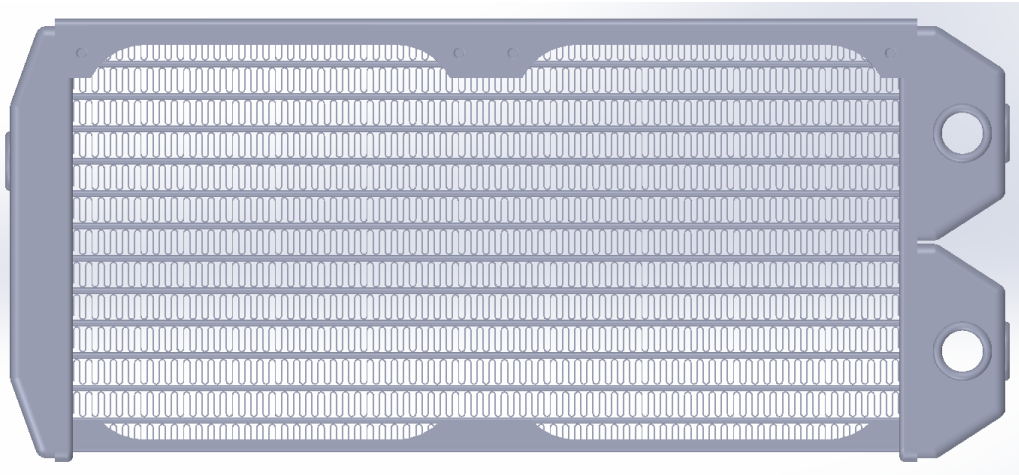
Vista frontal del radiador (caudal de aire perpendicular a la imagen). CAD proporcionado por el fabricante [14].
